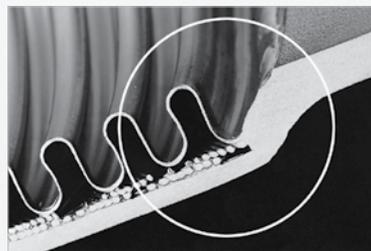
Sandure sans fissure ni bavure d'un flexible métallique
